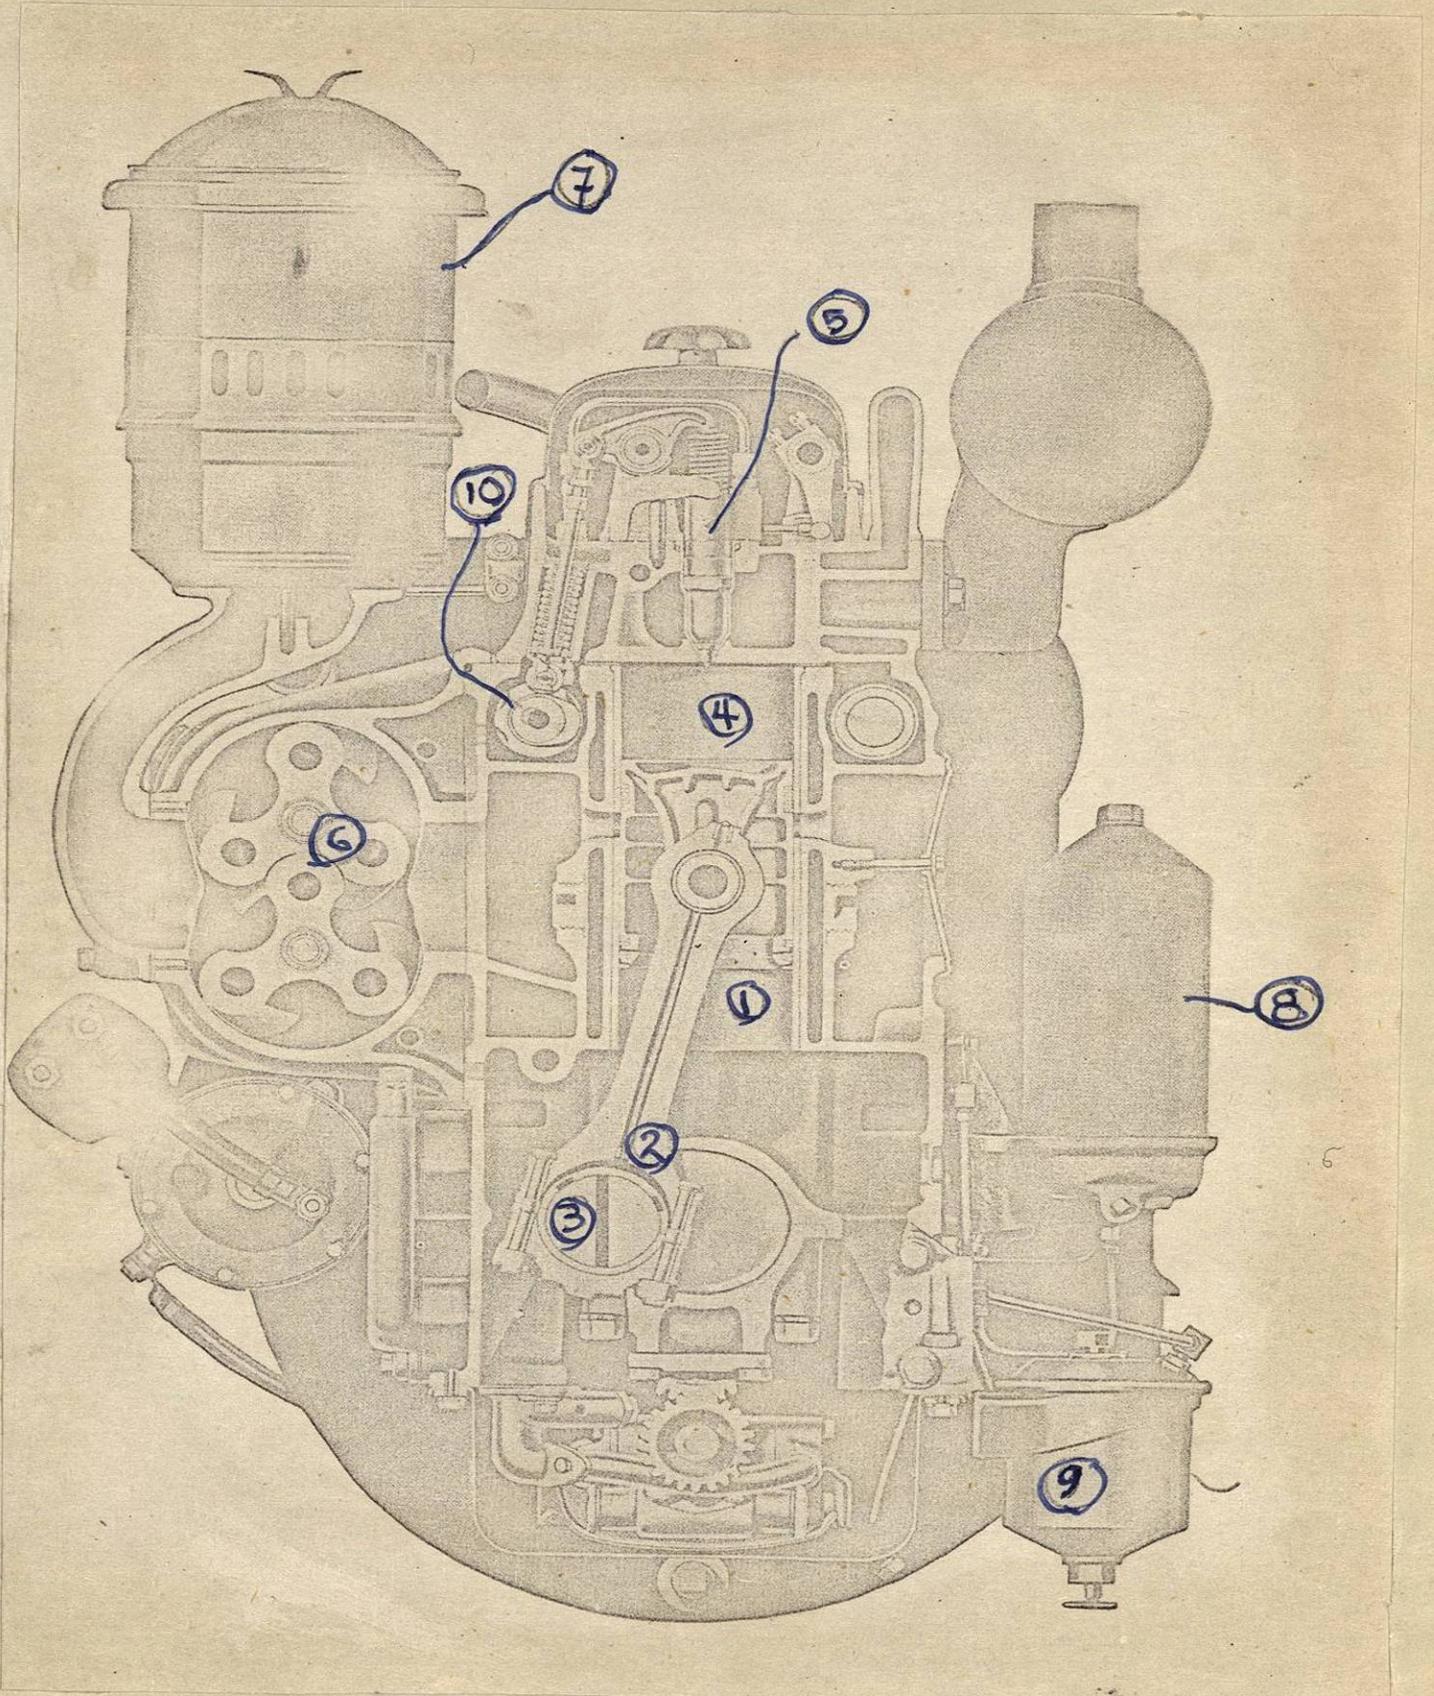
SECCIÓN TRANSVERSAL DE UN TÍPICO MOTOR INDUSTRIAL G.M.
